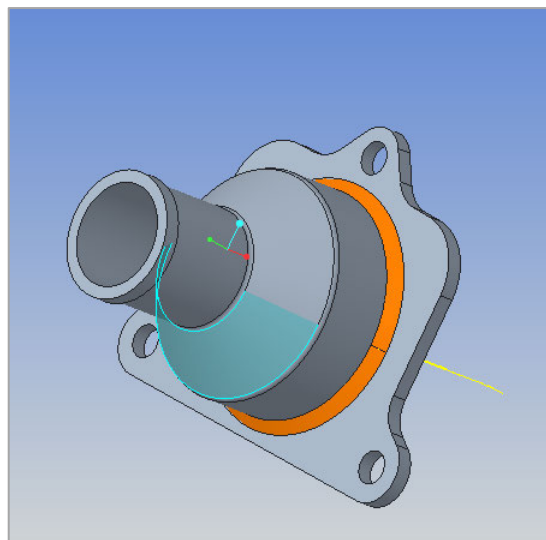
Flansch mit Rohr für den Austritt am AGR- Kühler
